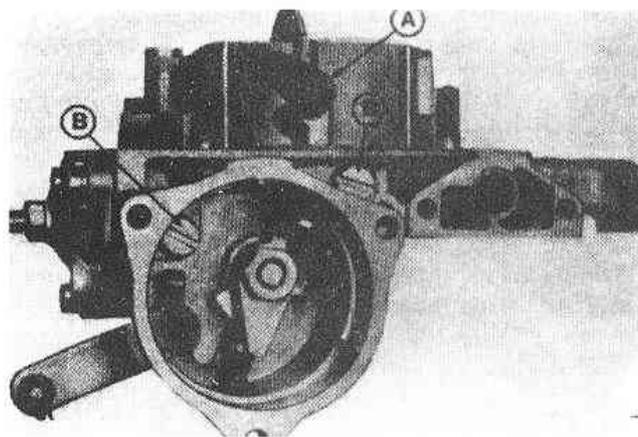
Снятие корпуса воздушной заслонки с верхней части корпуса карбюратора (Разд.37)
